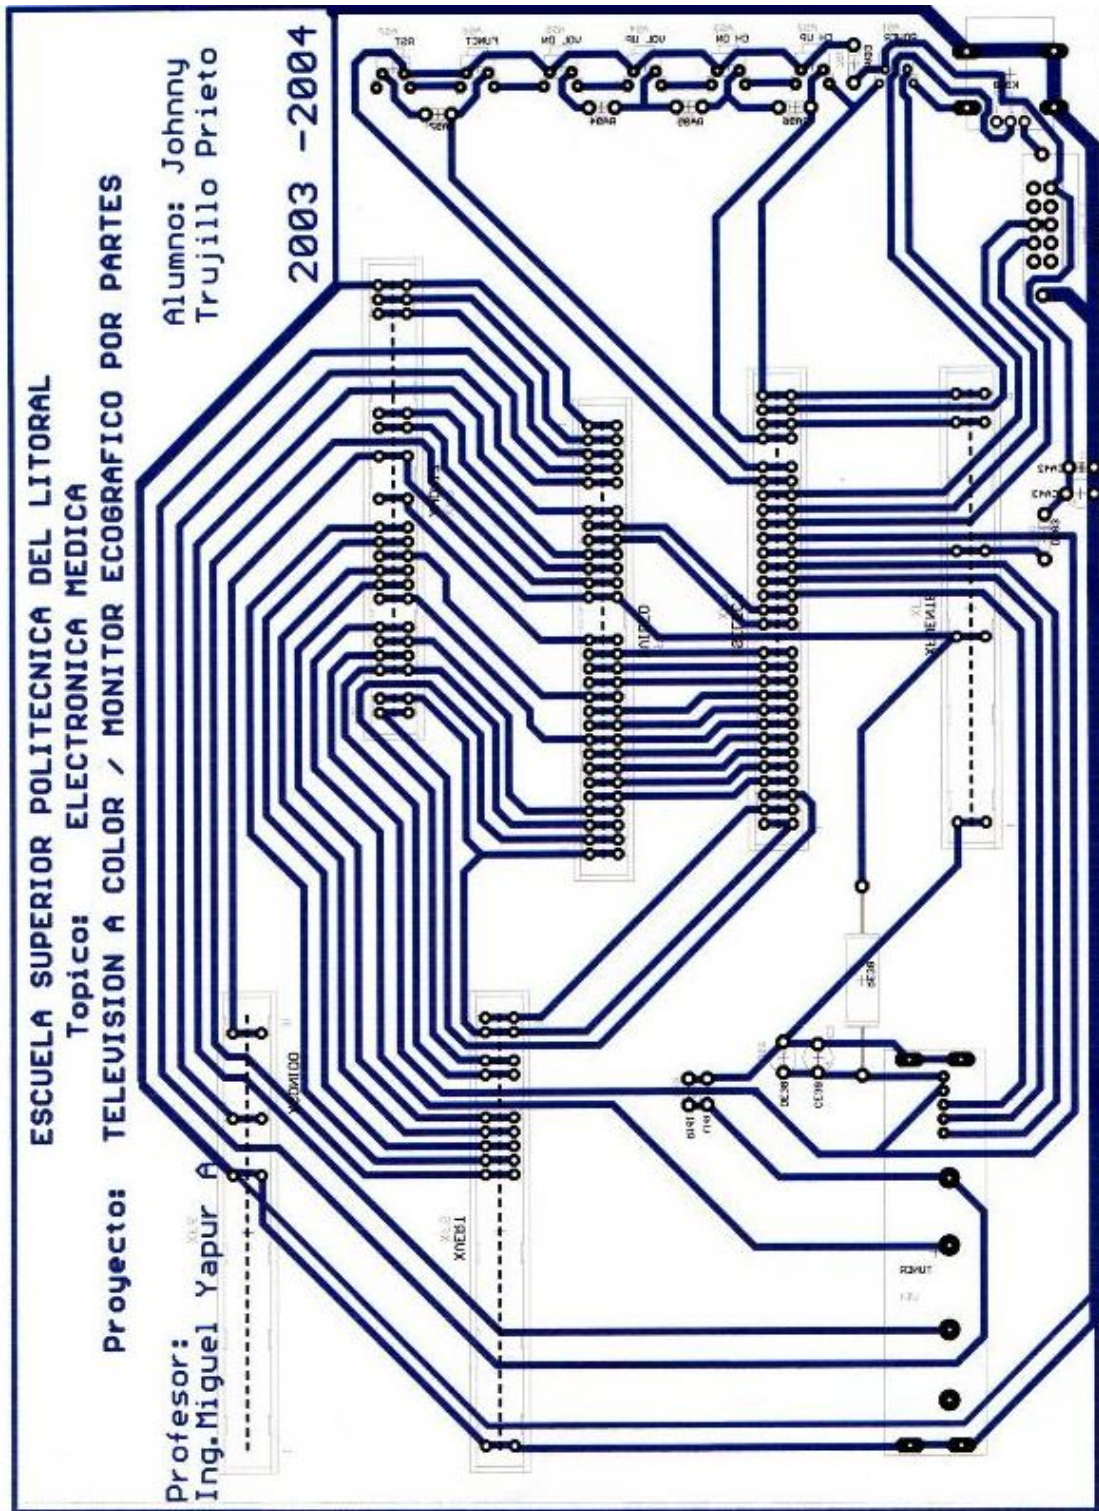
Sección PRINCIPAL trazado inferior
